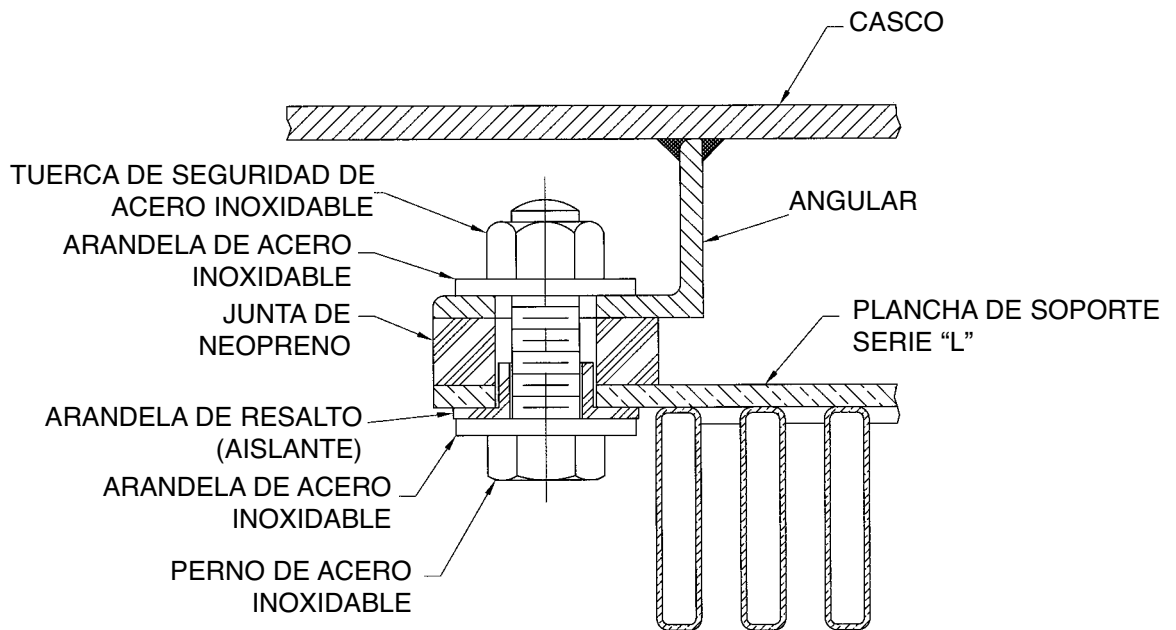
Plancha de soporte SERIE L con angular soldado al casco
